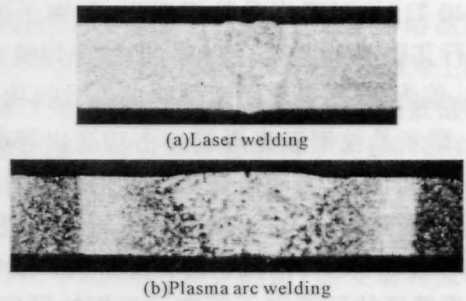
两种焊接方法焊接微米晶粒钢焊接接头宏观形貌
